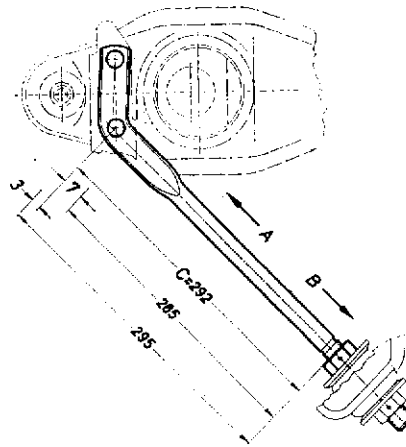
Exemple de réglage de la chasse à l'aide d'une jambe de force
